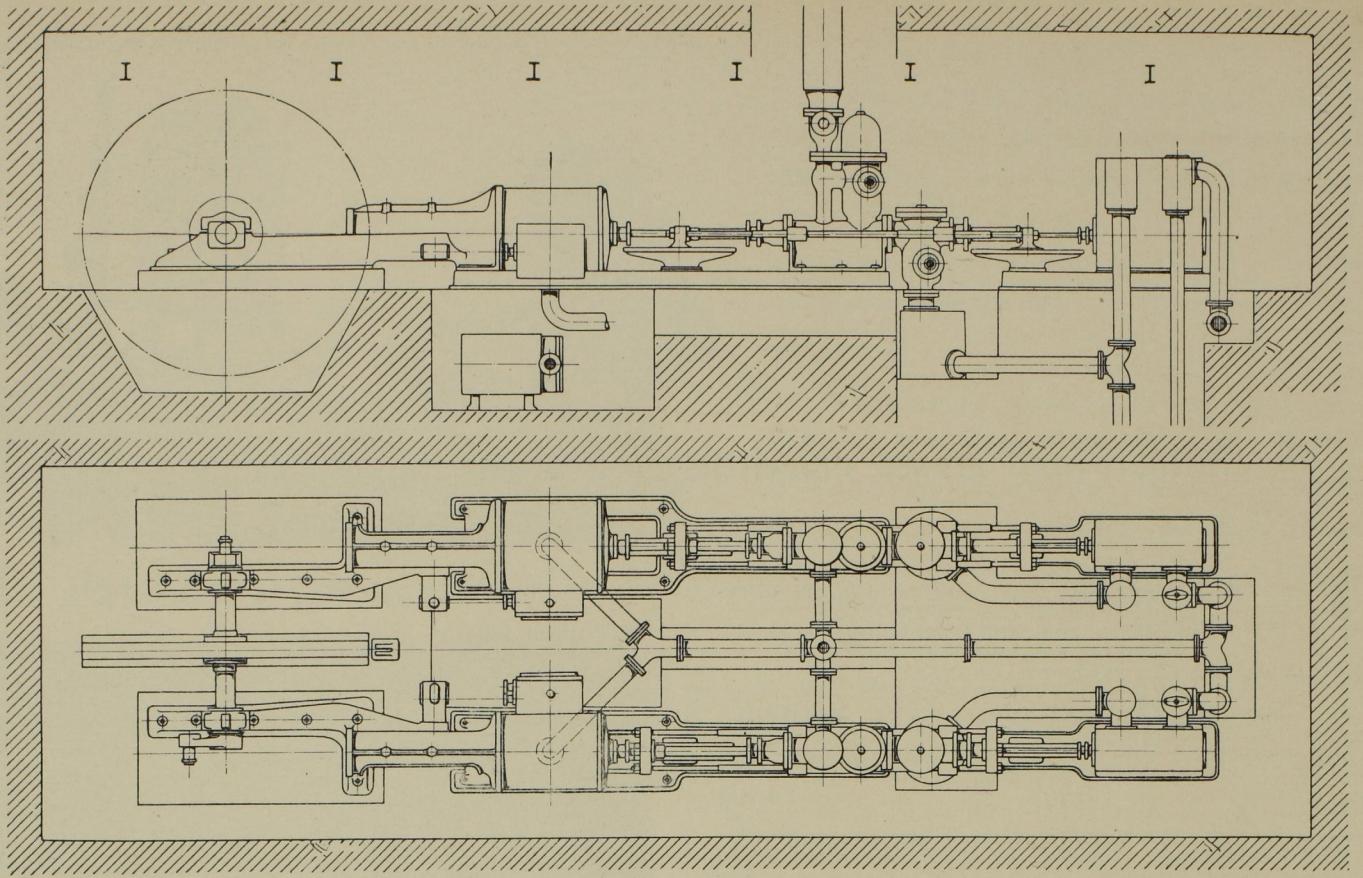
Seitenansicht und Grundriss. Masst. 1:100.
